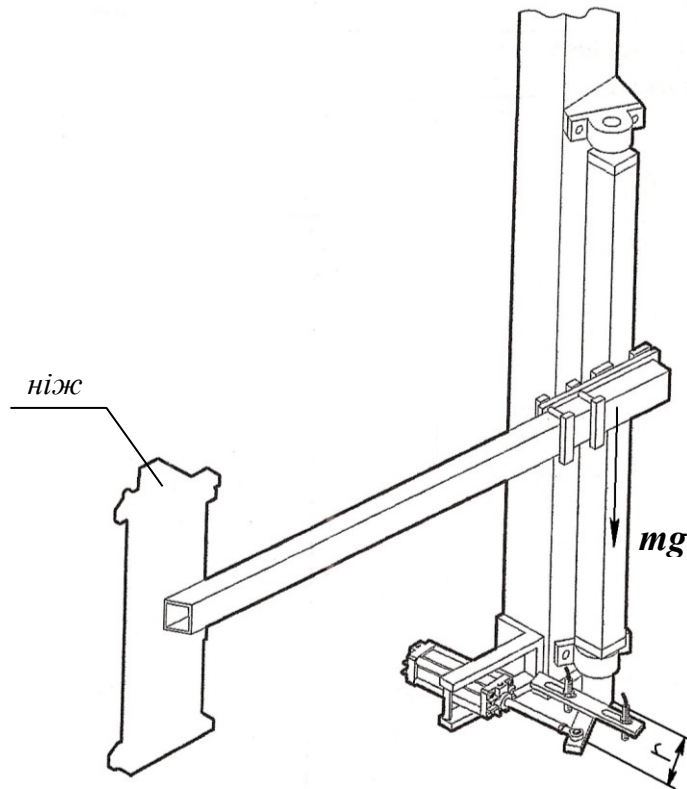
Розрахункова схема для механізму відрізання полімерної розтягнутої плівки
